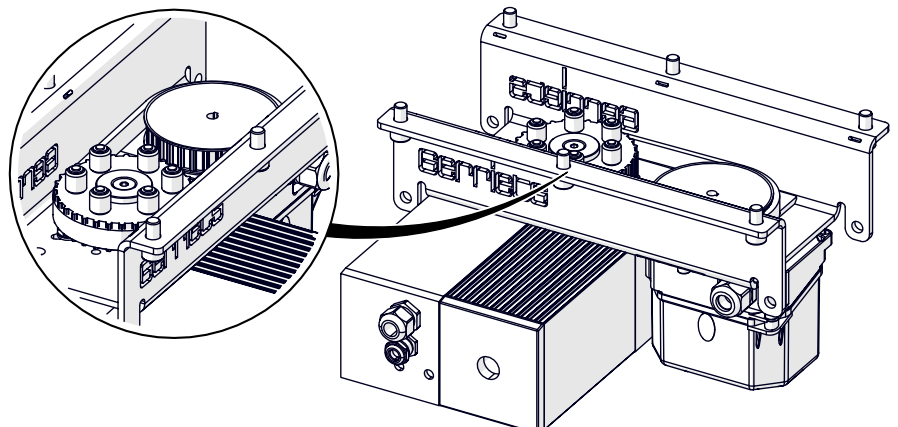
Kompakt-Getriebemotor – BELT DRIVE BT-12
